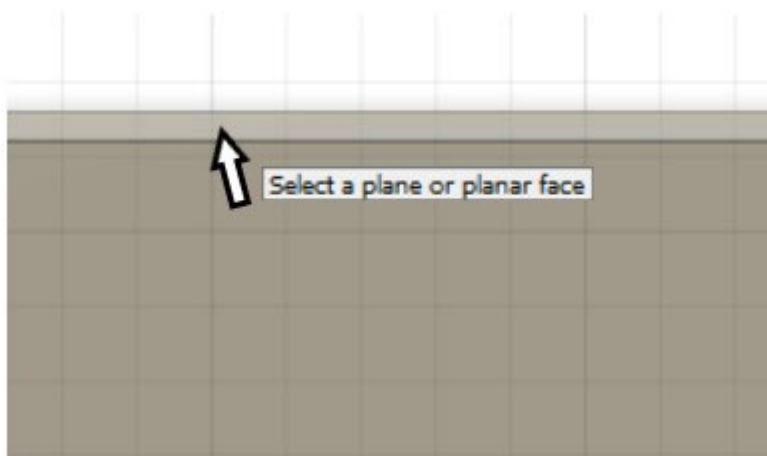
2 mm-Extrusion der Bodenplatte
